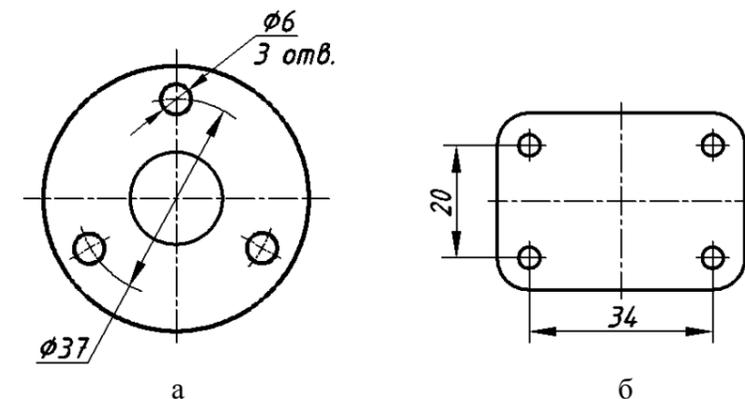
Нанесение размеров положения центров совмещаемых отверстий:
